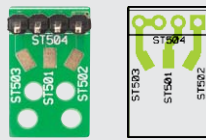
Platinenfoto und Belegungsplan der Steckerplatine
